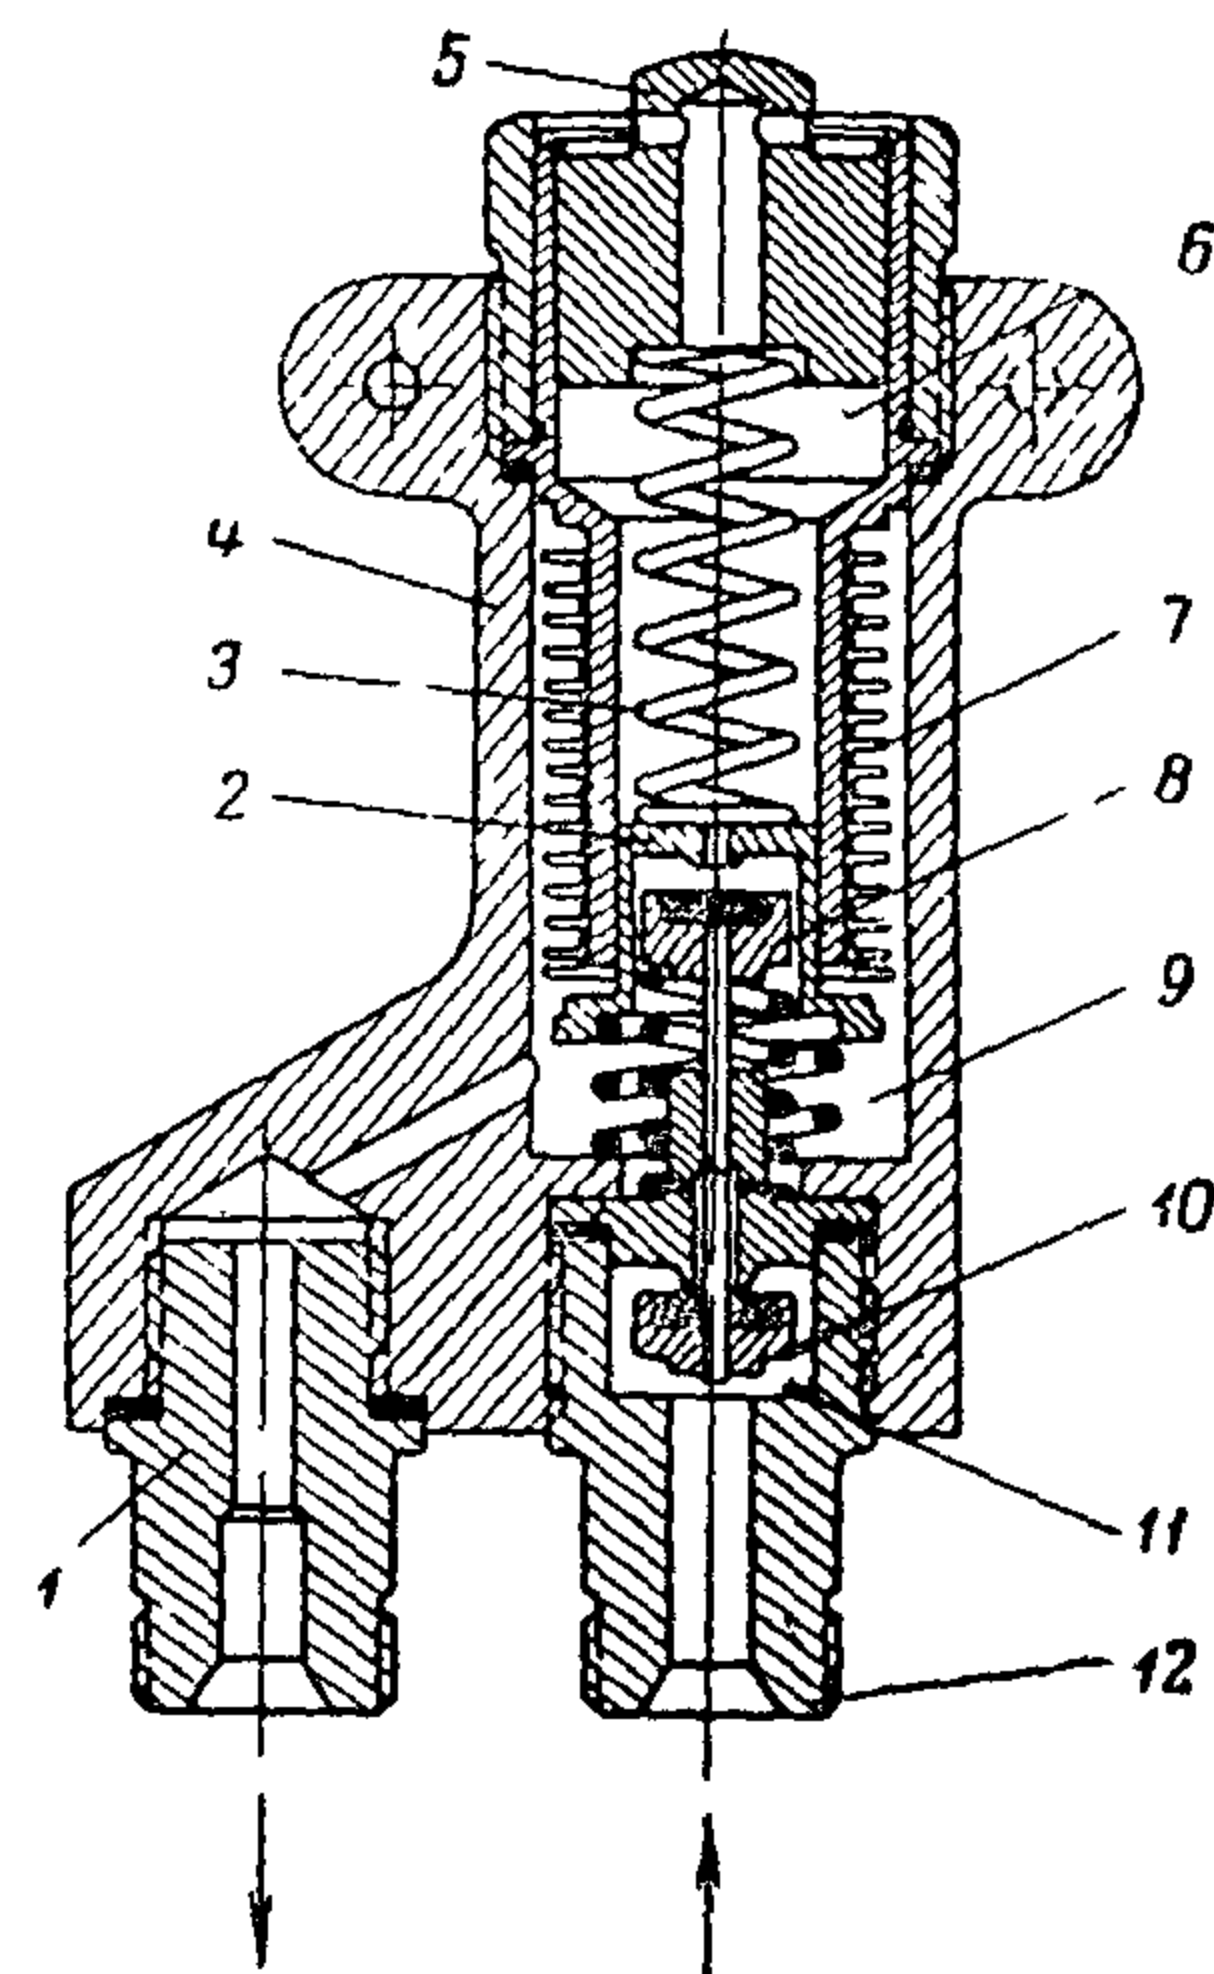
Редукционный клапан 51-7 (ПУ-6)
